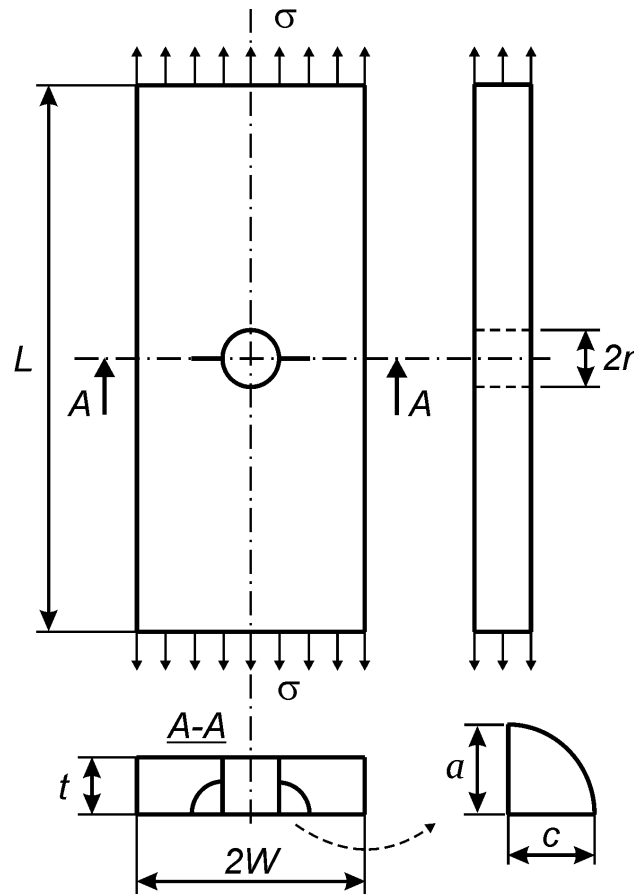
Образец с двумя угловыми четверть-эллиптическими трещинами
